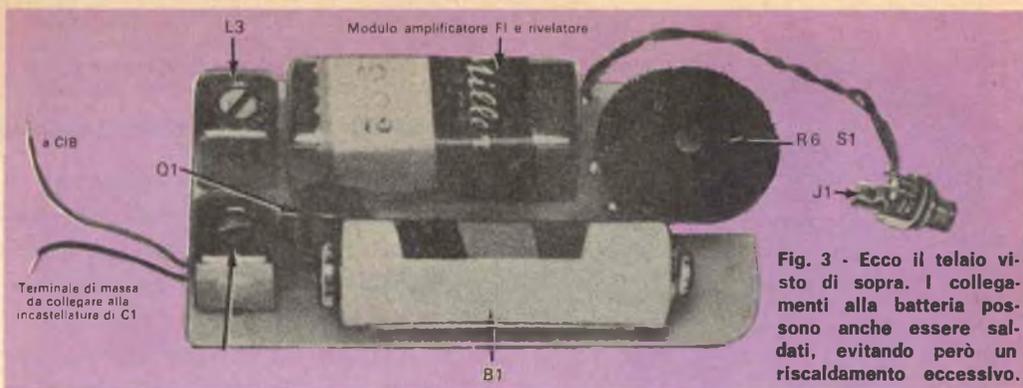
Ecco il telaio visto di sopra. I collegamenti alla batteria possono anche essere saldati, evitando però un riscaldamento eccessivo.
